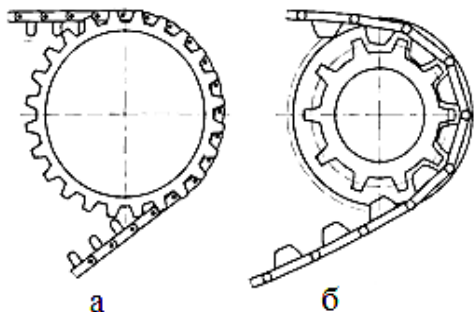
Цевочное (*а*) и гребневое (*б*) зацепления ведущего колеса с гусеницей
